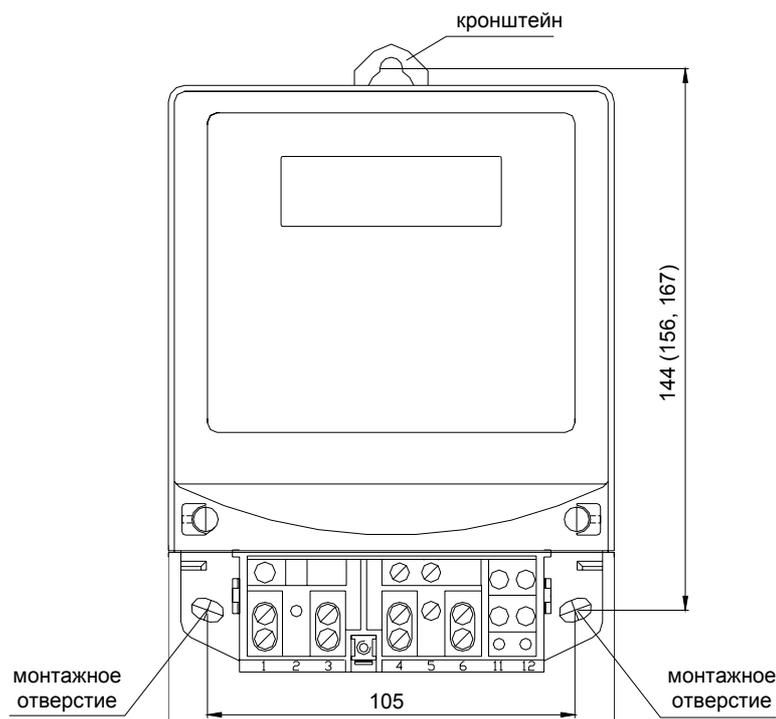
Общий вид счетчика без крышки колодки зажимов
